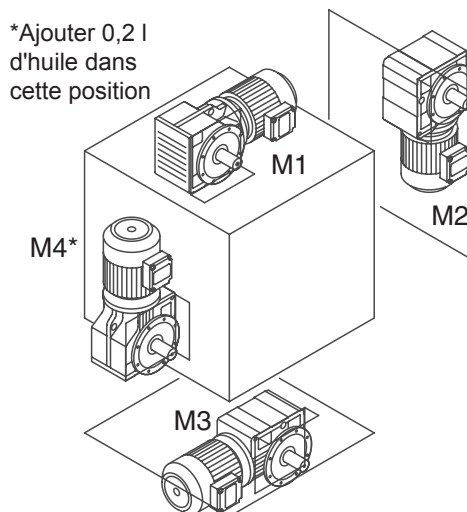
Positions de montage si le moteur est fourni par FlexLink
